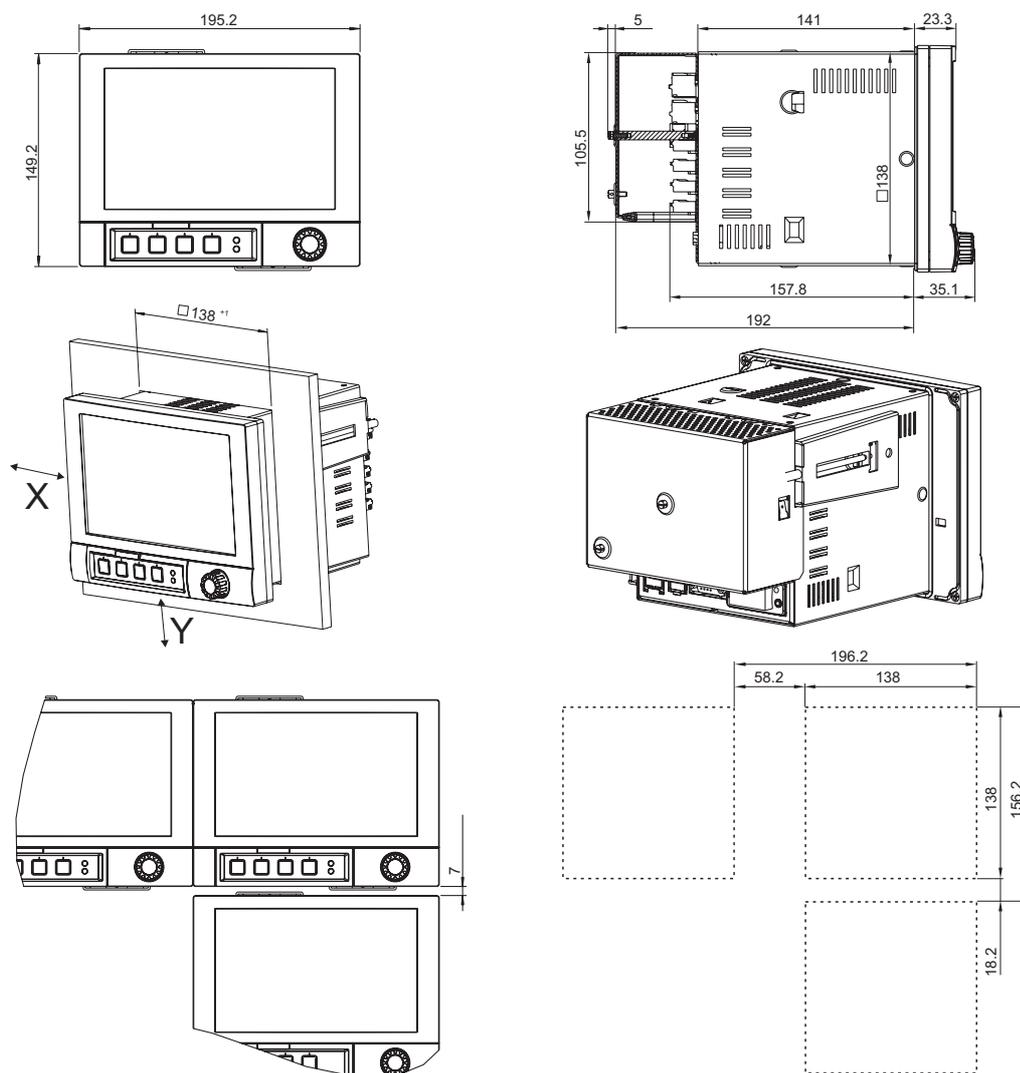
Montaggio a fronte quadro, dimensioni di installazione. Tutte le dimensioni sono in mm.
